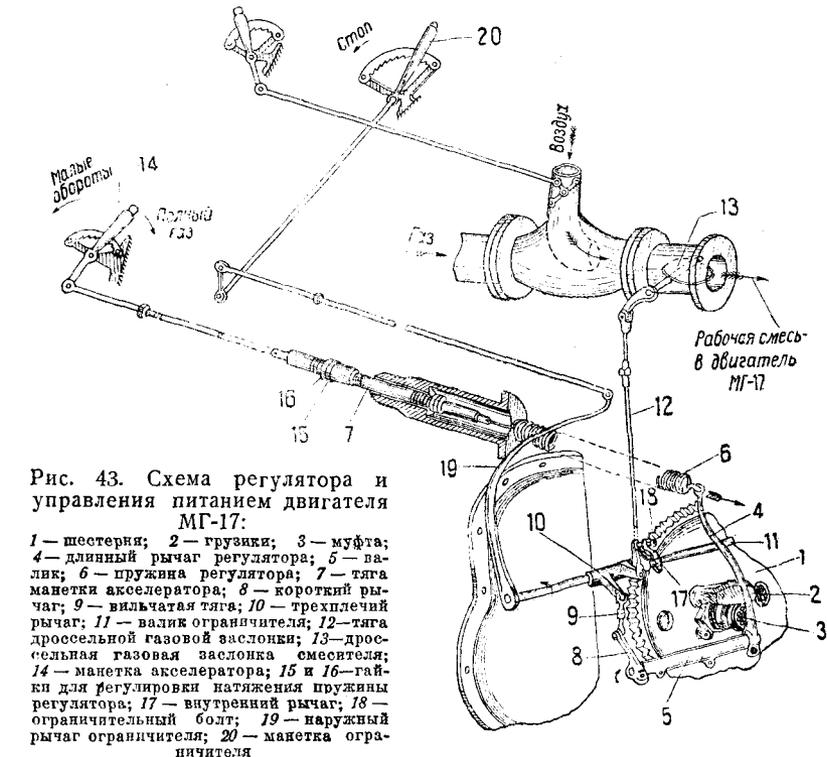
Схема регулятора и управления питанием двигателя МГ-17:
